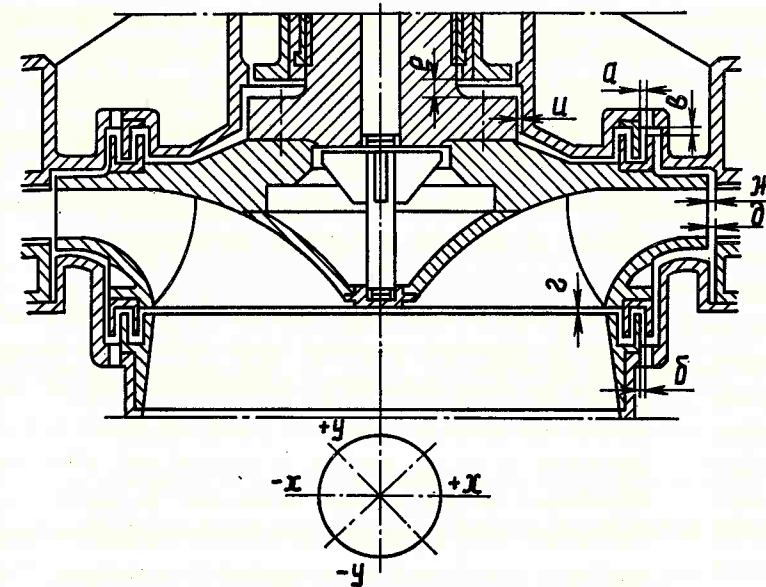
Формуляр на установку рабочего колеса высоконапорной радиально-осевой гидротурбины
